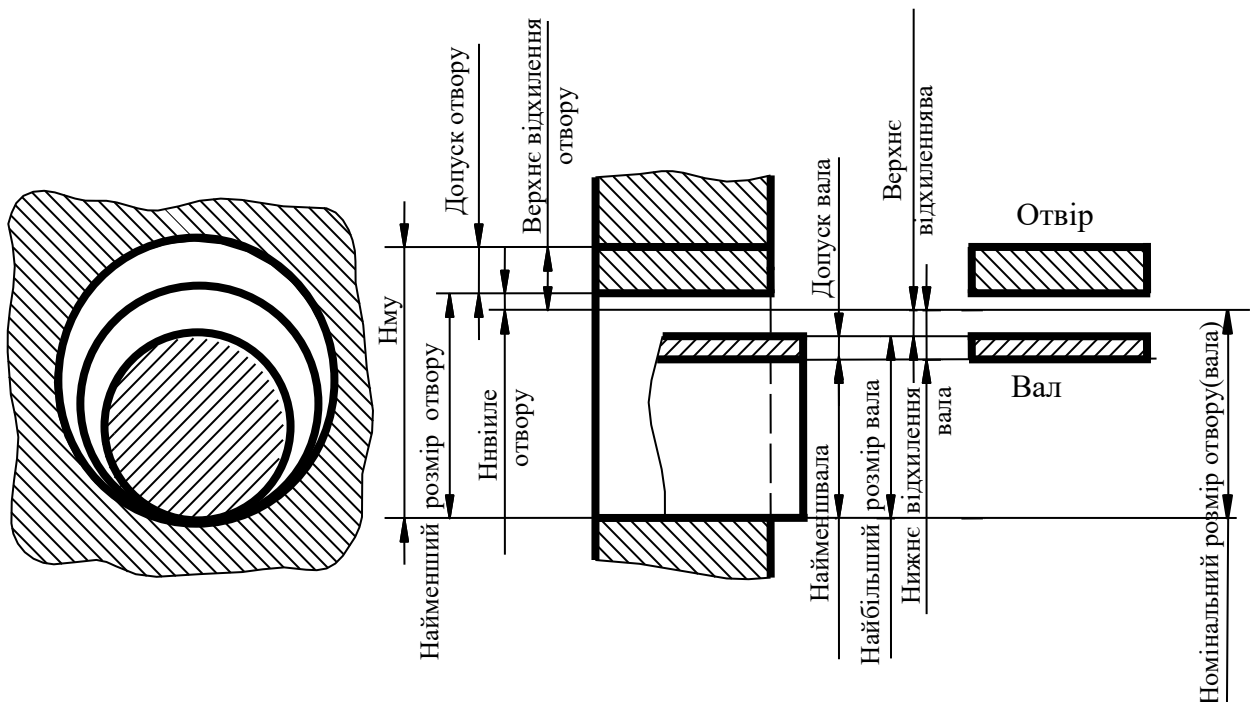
Поля допусків отвору і вала в з'єднанні із зазором (відхилення отвору додатні, відхилення вала від'ємні)
